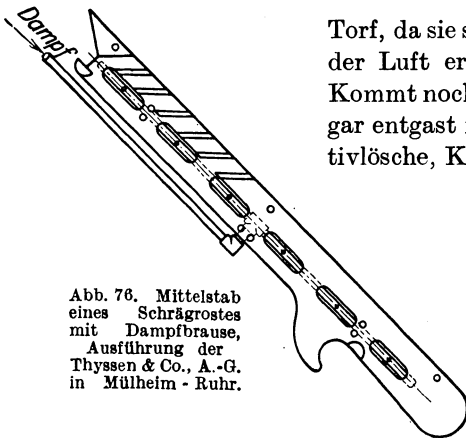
Mittelstab eines Schrägrostes mit Dampfbrause, Ausführung der Thyssen & Co., A.-G. in Mülheim - Ruhr.
